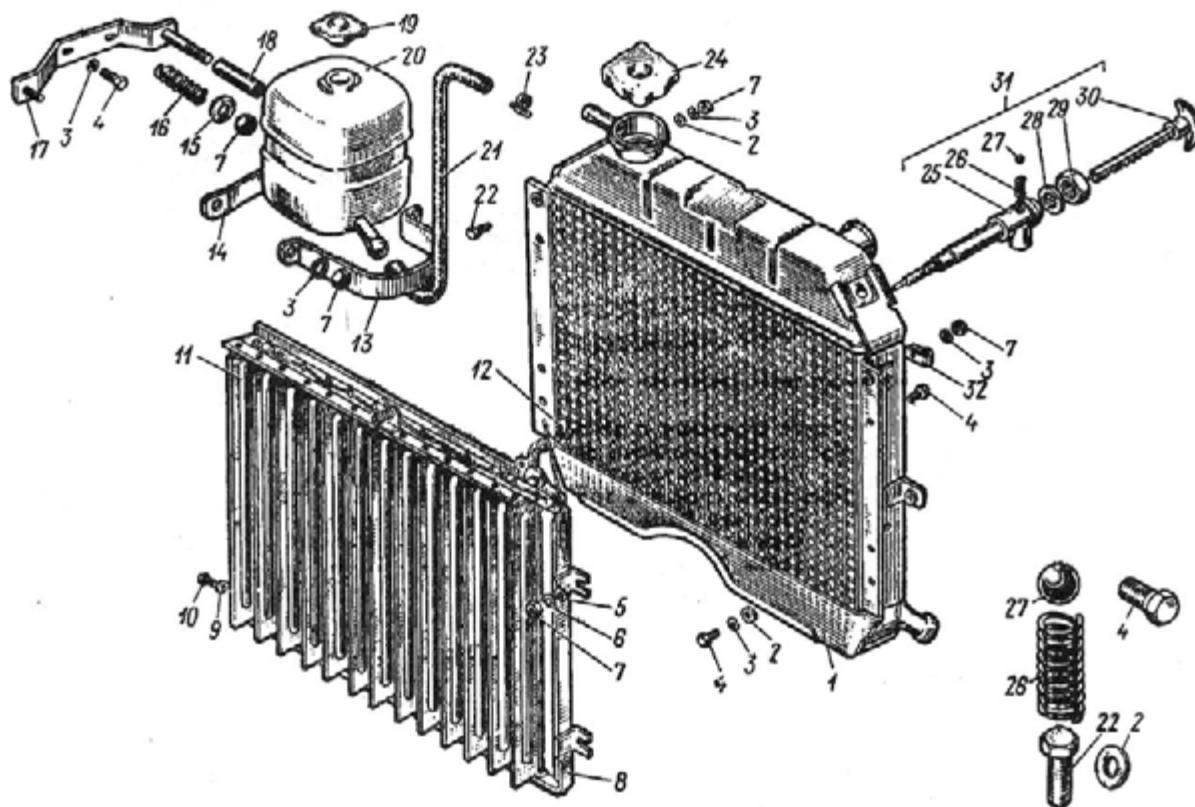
Радиатор (с пробкой горловины), жалюзи, расширительный бачок и детали их крепления
